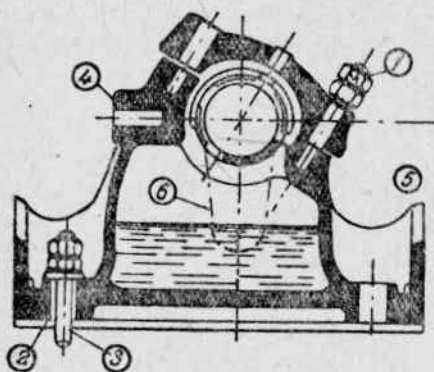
Коренной подшипник коленчатого вала Людиновского завода.
